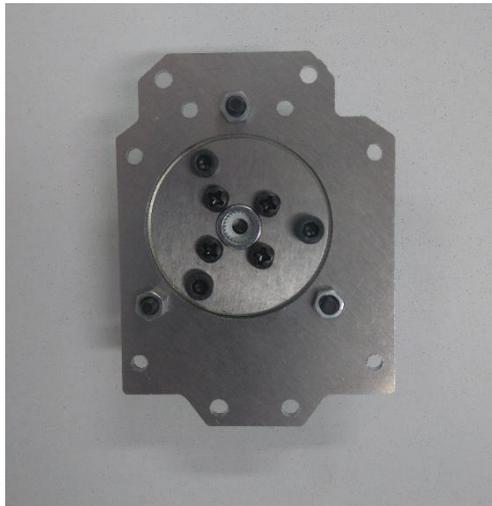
CONJUNTO PASO 2 VISTA 1
